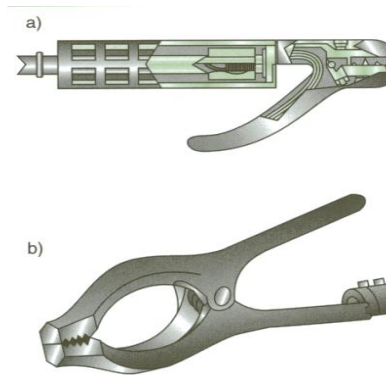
Pinzas de acoplamiento entre el equipo y la pieza a soldar.
